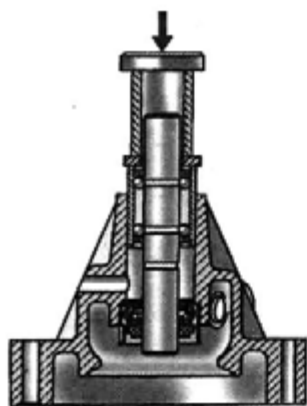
Запрессовка подшипника с валиком водяного насоса в корпусе
